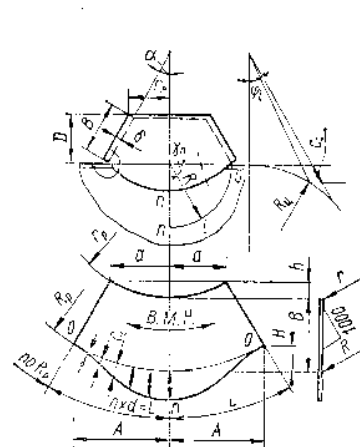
Нормальный конический штуцер на цилиндрической поверхности.
